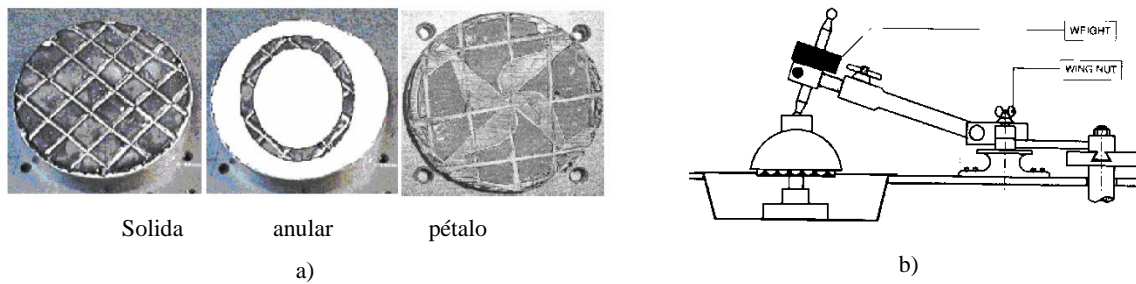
a) Herramientas de desgaste; b) Máquina pulidora.
